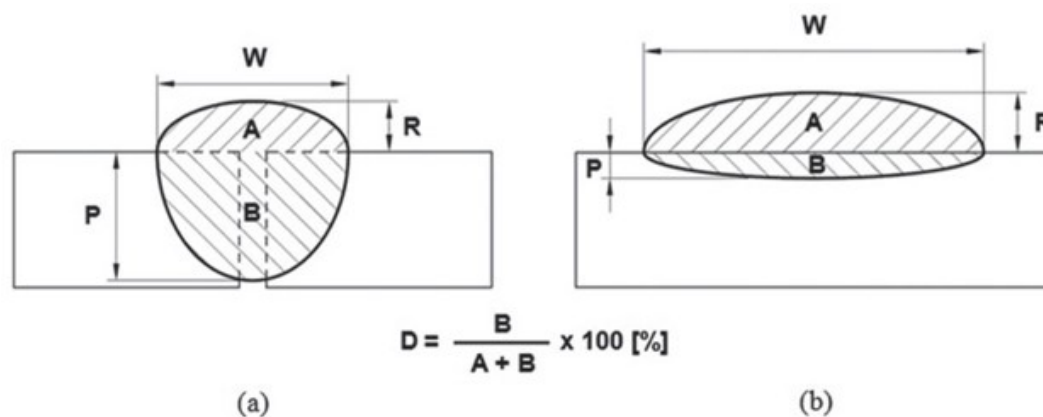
Perfil geométrico desejado do cordão de solda: a) união da junta soldada (aplicações convencionais); b) soldagem de revestimento
